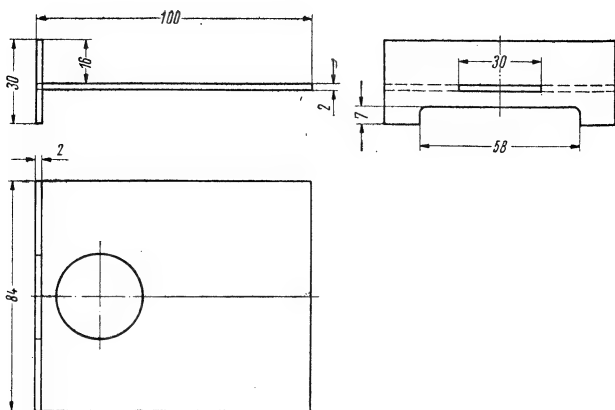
Konstruktive Ausführung der Chassisplatte (Lochdurchmesser und Form der Aussparung sind nach dem verwendeten Lautsprecher festzulegen)
